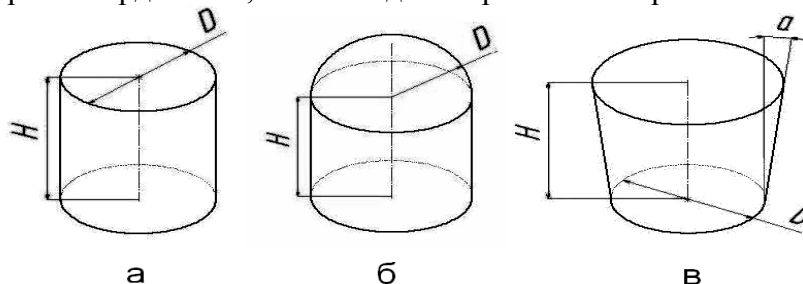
Конфигурация прибылей: а) цилиндрическая; б) полушаровая (с цилиндрической частью); в) коническая
